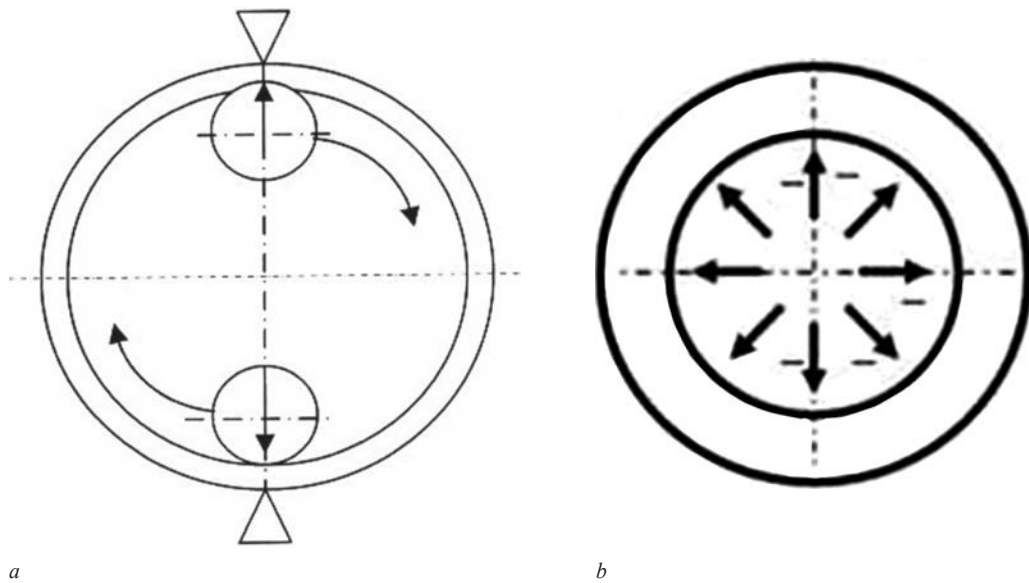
Конструктивная схема устройства для стабилизации кольцевых заготовок типа фланец:
